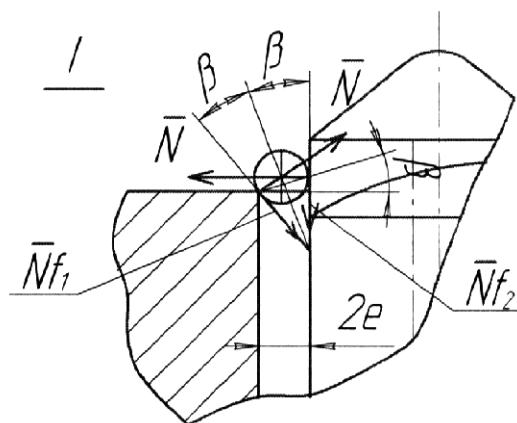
Умова запобігання заклинюванню оброблювальної кульки
